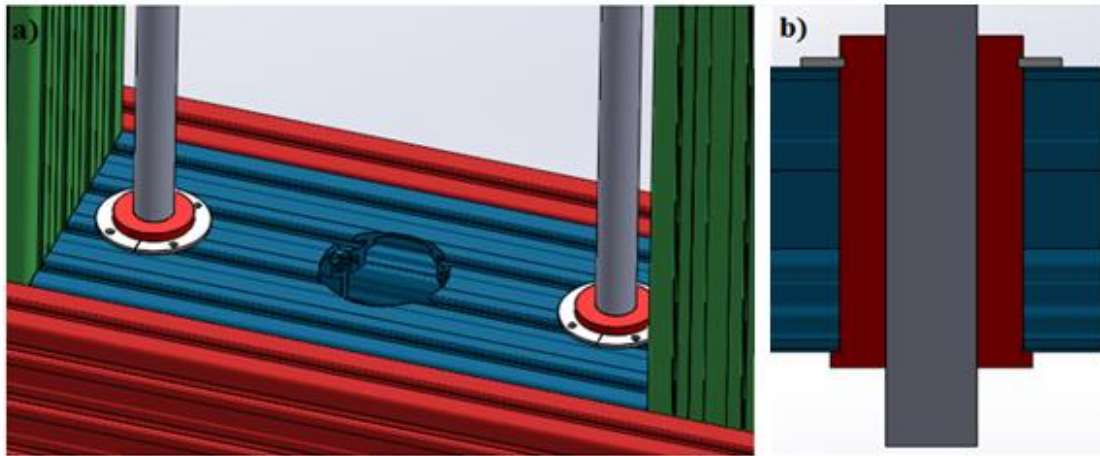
a) Fixação das guias a estrutura (parte de baixo); b) Vista em corte da fixação do casquilho inferior e guia
